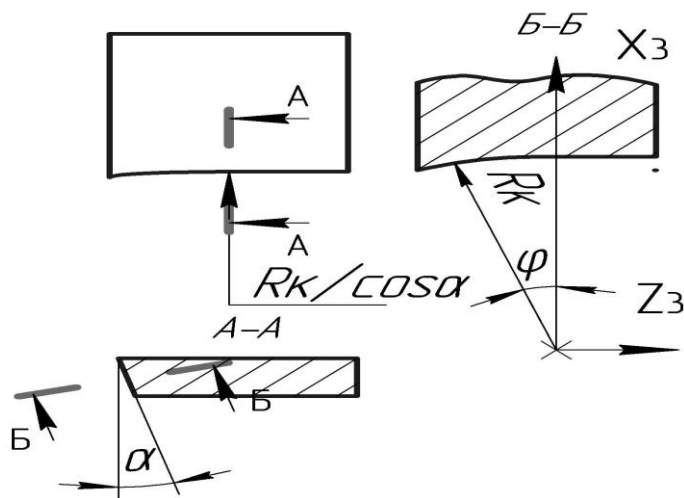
Эскиз режущей части инструмента с криволинейной режущей кромкой
